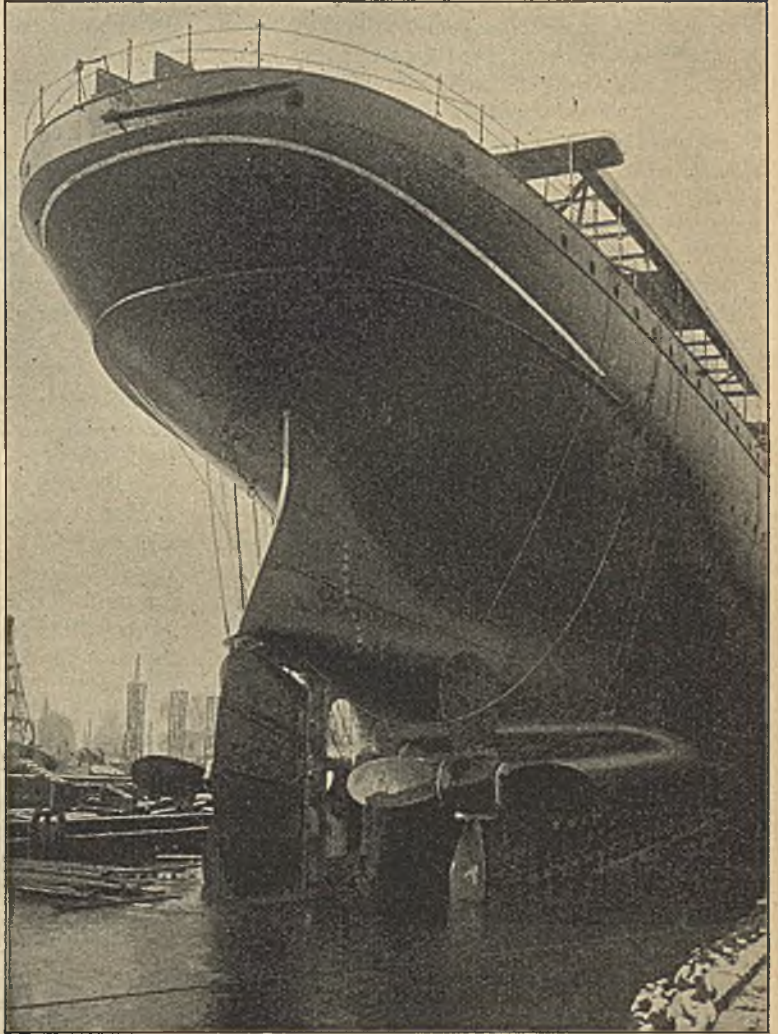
Heckansicht des Schiffes mit den Schrauben.
